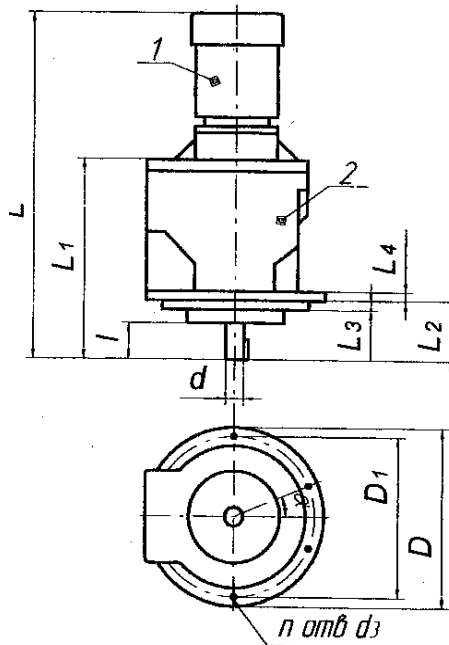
Мотор-редуктор типу МПО1: 1-електродвигун; 2-планетарний редуктор
